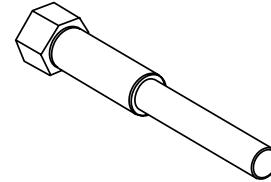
Demontagewerkzeug für obere Kupplung (Primäriemenscheibe)
